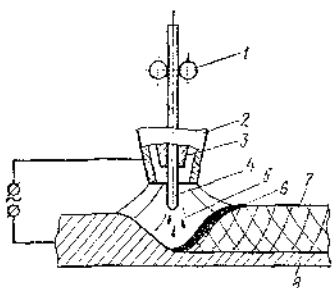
Схема автоматической и полуавтоматической аргонодуговой сварки плавящимся электродом
